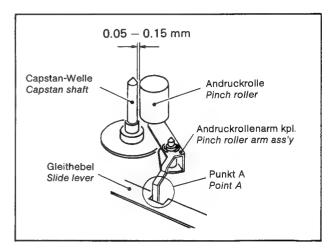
Andruckrollenabstand Fig. 2-22 Pinch roller spacing
